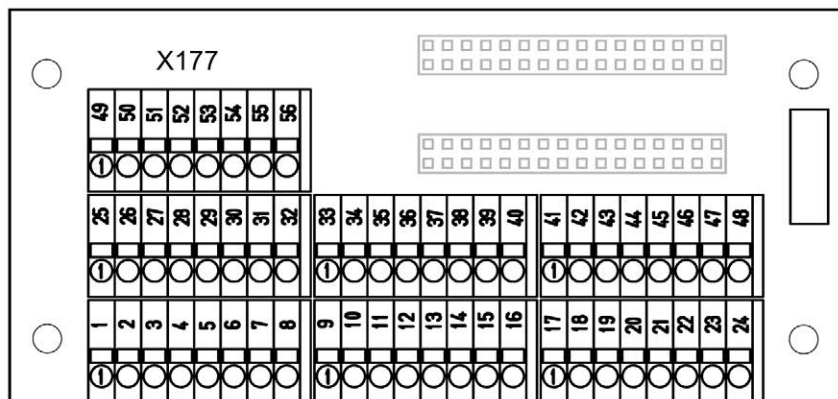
Disposición de bornes/conectores en la "Connector Board"
